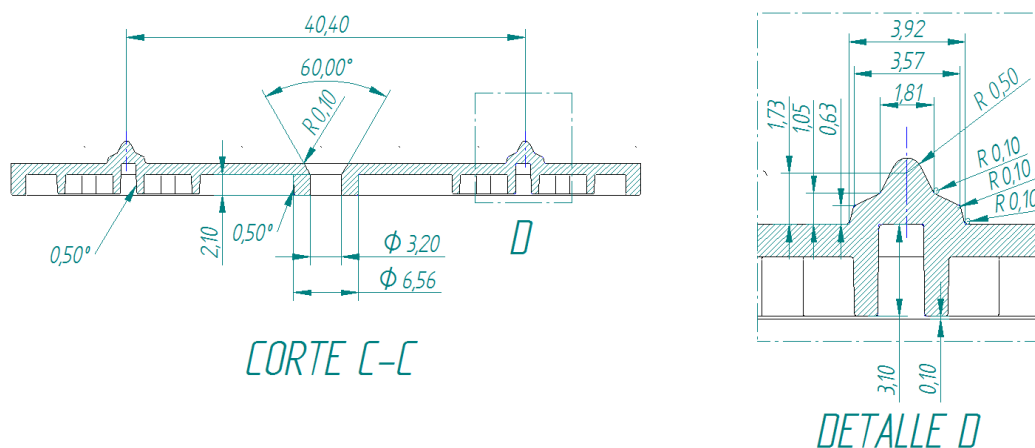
Detalle de espesor de pared en traviesas y zona de raíles
